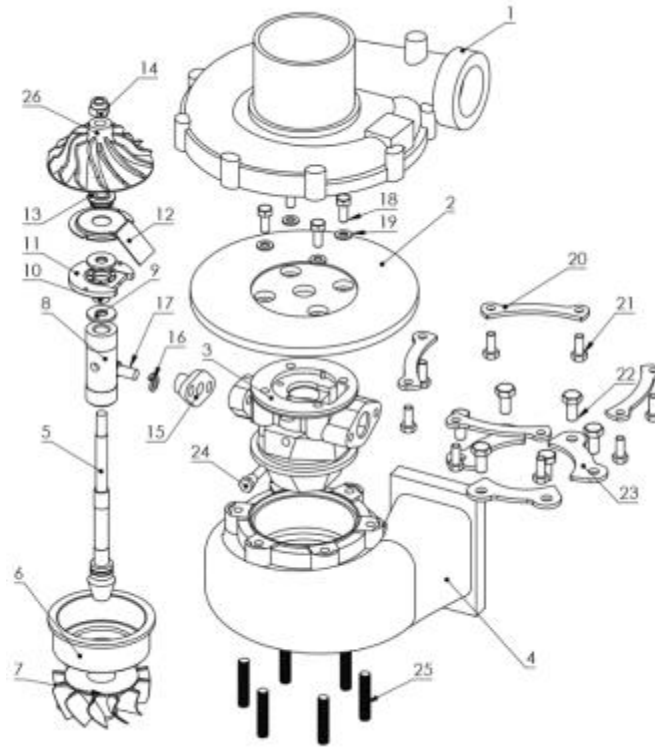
Vista explosionada de ensamblaje *TKP-100
